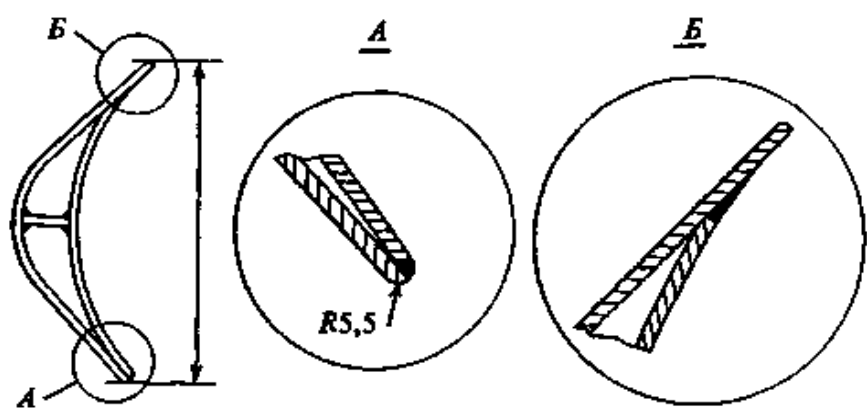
Сварно-штампованная сопловая лопатка ХТЗ (сечение лопатки)
